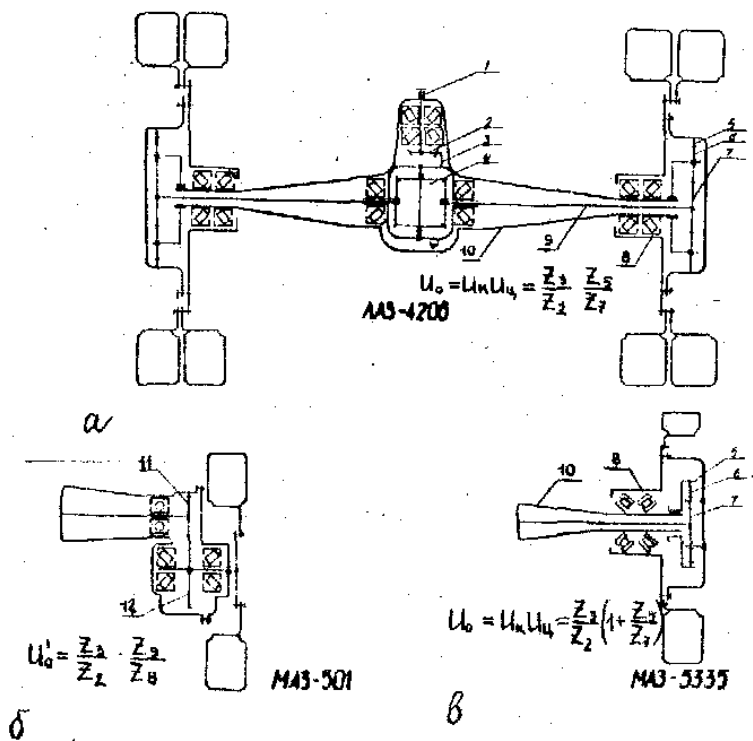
Схеми подвійних рознесених головних передач: а, в – з колісною передачею; б – з бортовою передачею; 1 – вал ведучої конічної шестерні; 2 – ведуча конічна шестірня; 3 – ведена конічна шестірня; 4 – диференціал; 5 – епіциклічна шестерня; 6 – сателіт; 7 – сонцева (центральна) шестерня; 8 – маточина колеса; 9 – піввісь; 10 – балка ведучого моста; 11 – ведуча циліндрична шестерня; 12 – ведена циліндрична шестерня
